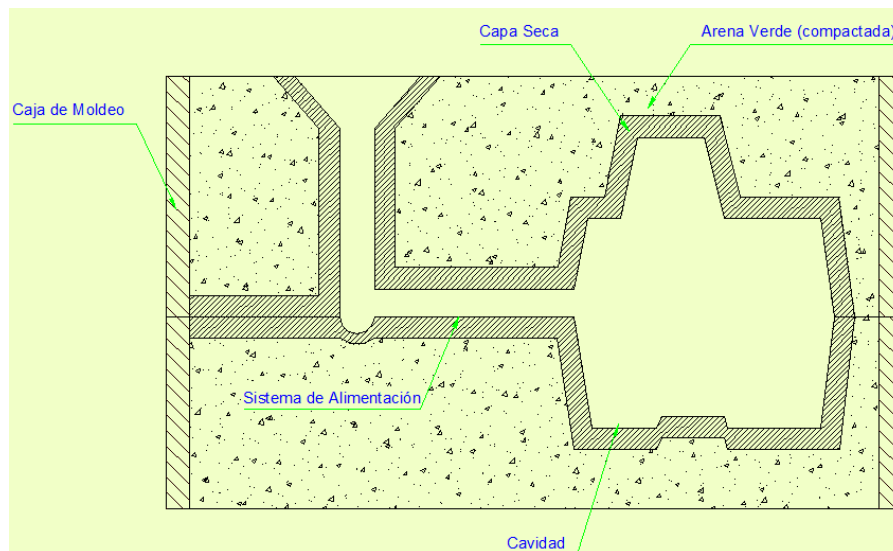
Corte transversal de caja moldeo cerrada con capa seca.
